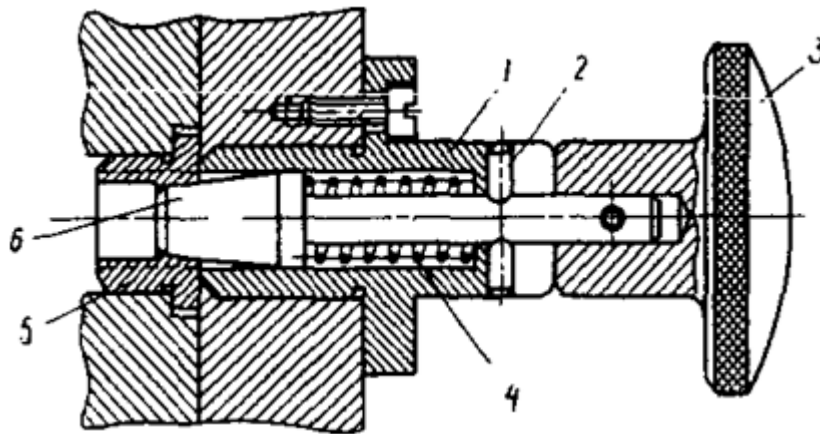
Витяжний конусний фіксатор розподільчого пристрою
